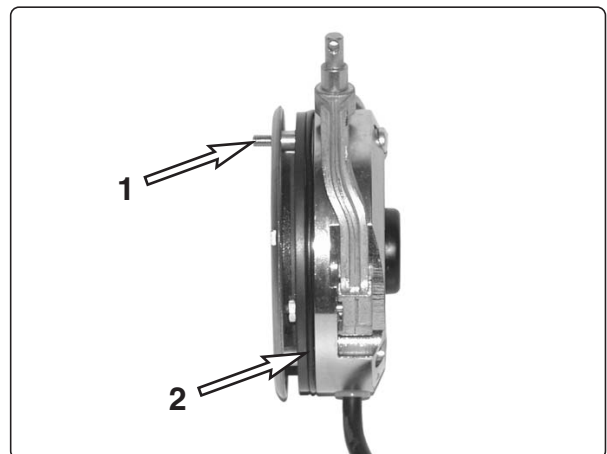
Teile mit der Schraube (1) aufeinander ausrichten. Der O-Ring muss richtig in seiner Aussparung liegen.
